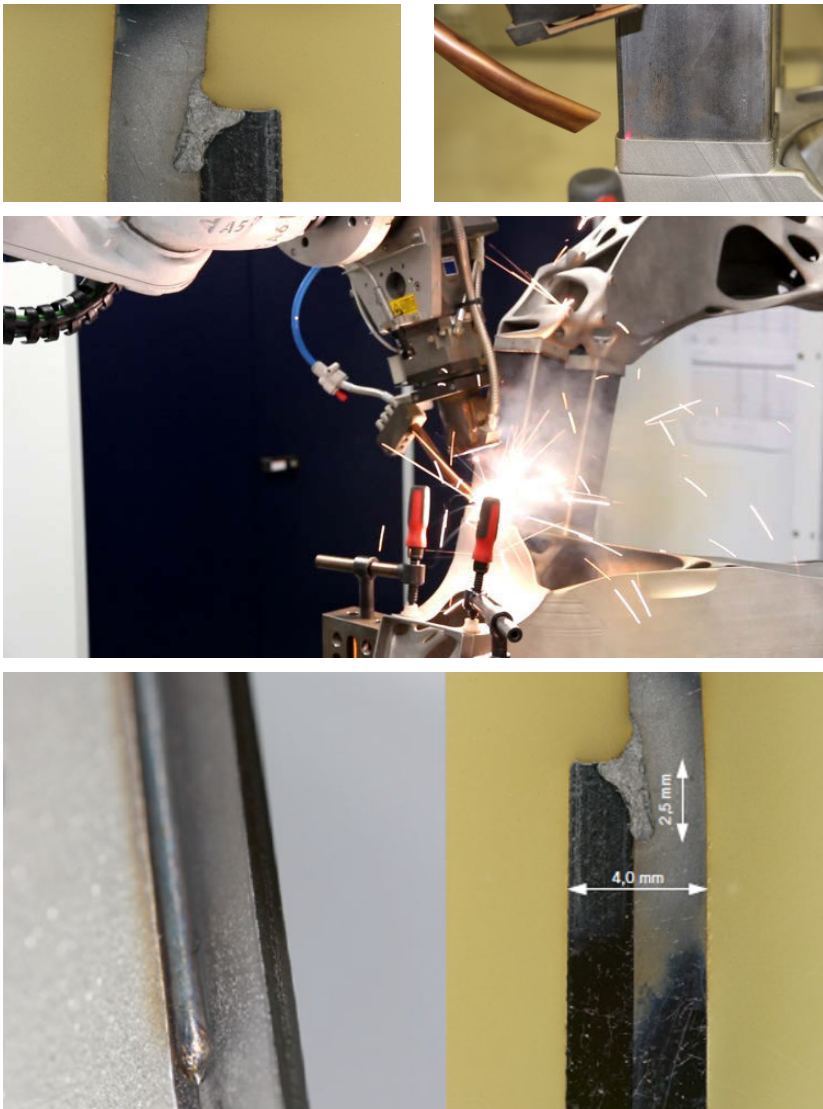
Laserschweißen: Die Laserschweißtechnik in Kombination mit dem prozessgerechten Bauteildesign ermöglicht ein hochpräzises Fügen der filigranen Leichtbaustrukturen bei minimalem Wärmeverzug.
